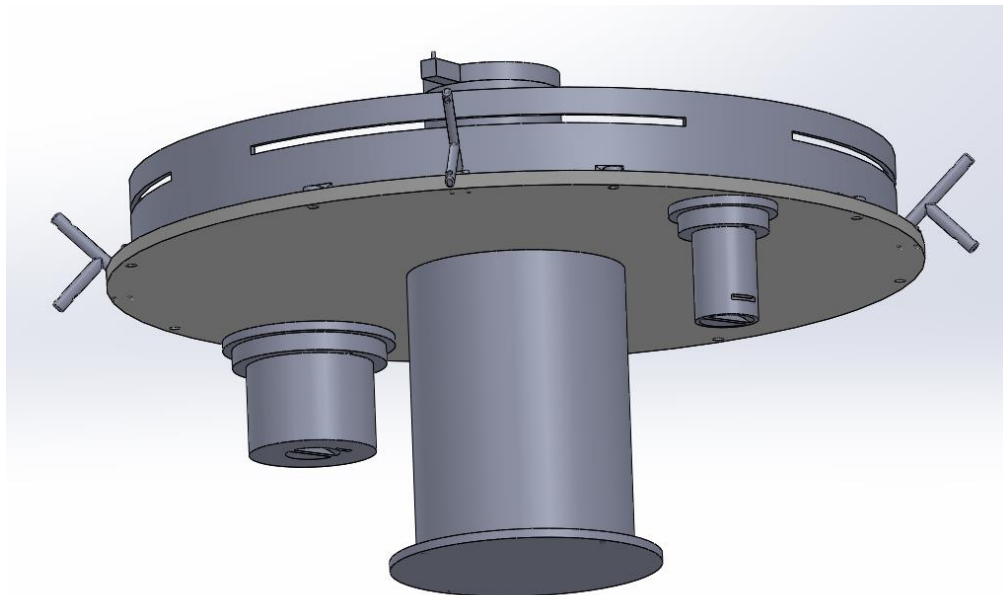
Conjunto após a montagem dos recipientes para os componentes eletrônicos
